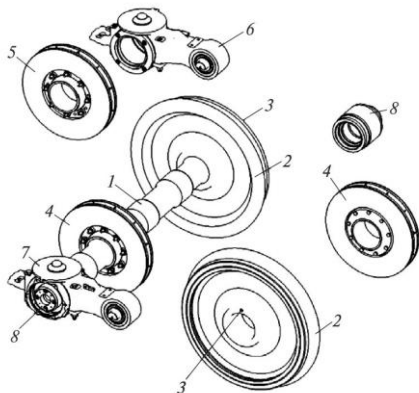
Составные части колесной пары немоторной тележки ВСП «Сапсан»: 1 – ось; 2 – колесо; 3 – резьбовая заглушка; 4, 5 – тормозные диски; 6 – буксовый балансир с сайлент-блоком; 7 – буксовый балансир с буксой 8 и сайлент-блоком
